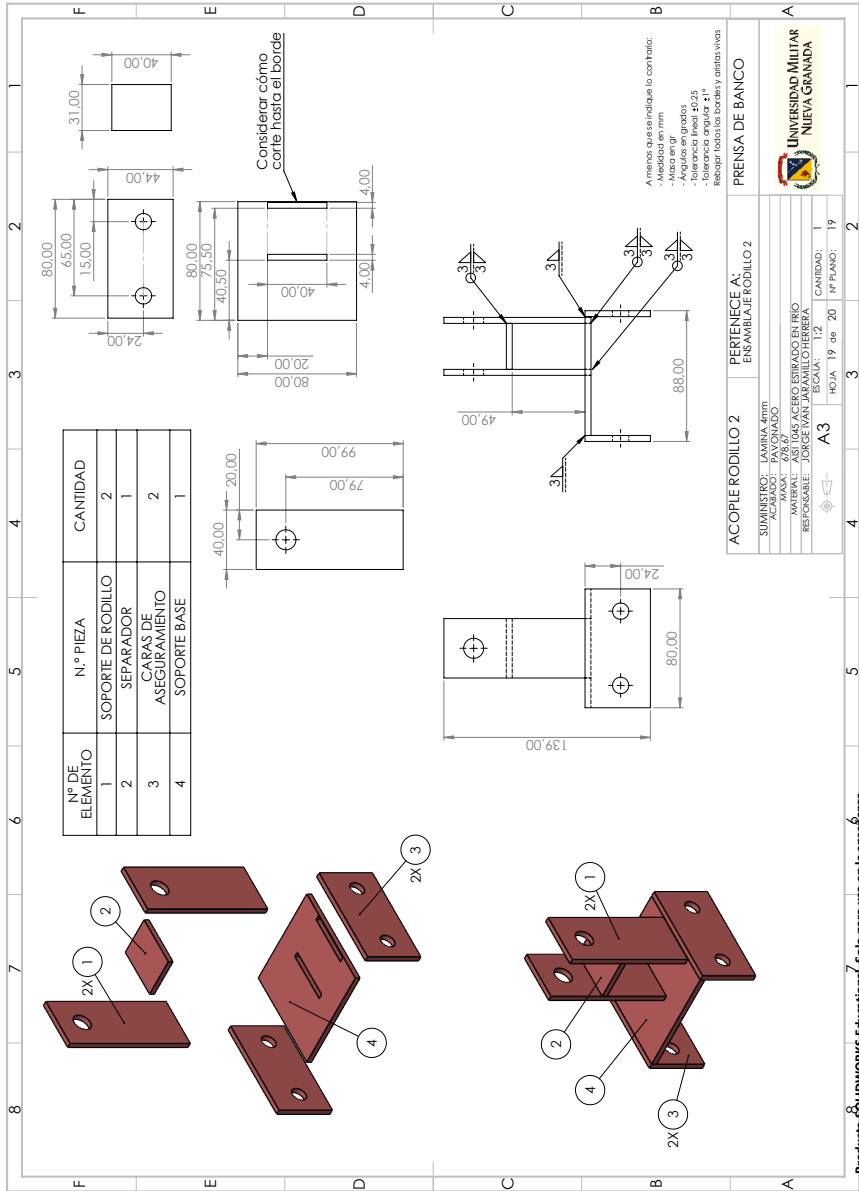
Plano 019, de la pieza "Acople Rodillo": Modelo CAD y plano elaborado por el autor mediante la herramienta de pieza y dibujo de "Solidworks".
